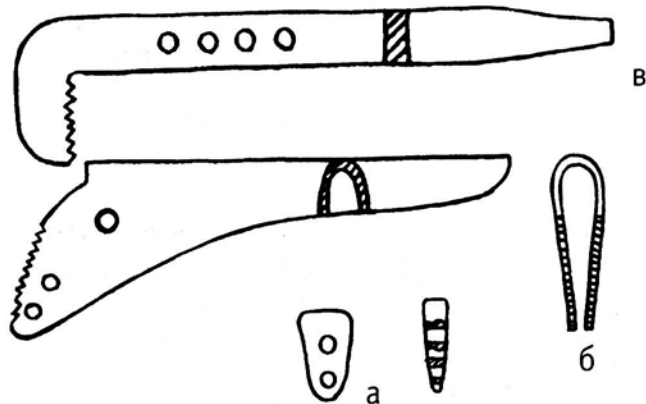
Основные детали ключа переставного двухрычажного английского типа: а — «сухарь»; б — неподвижный рычаг; в — подвижный рычаг
